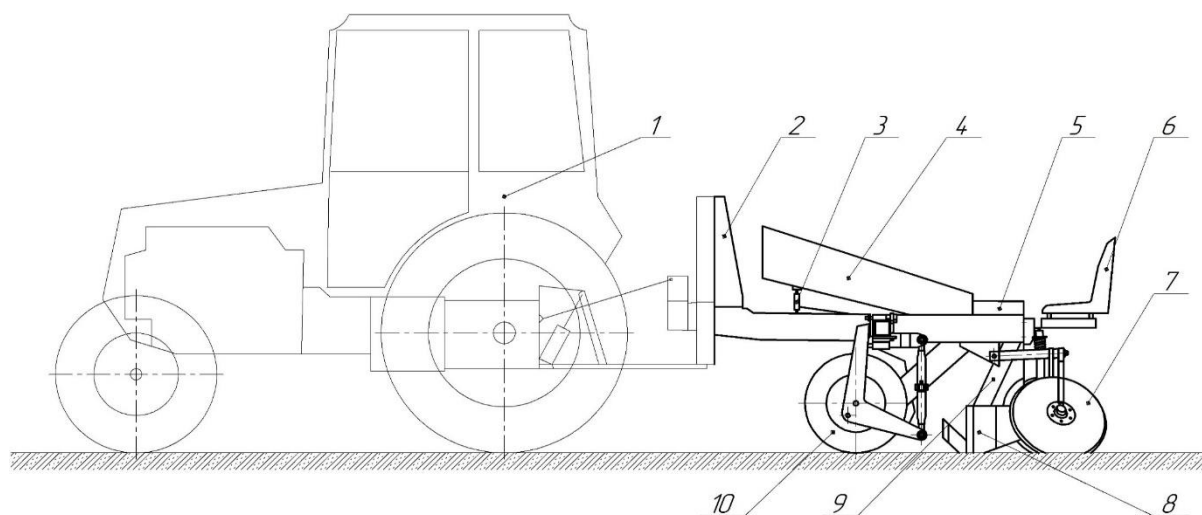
Принципиальная схема полуавтоматической посадочной машины: 1-трактор; 2-автосцепка; 3-гидроцилиндр; 4-загрузочная платформа; 5-высаживающий аппарат; 6-сидение; 7- заделывающие рабочие органы; 8-сошник; 9-направляющий кожух; 10-опорно-приводное колесо.
